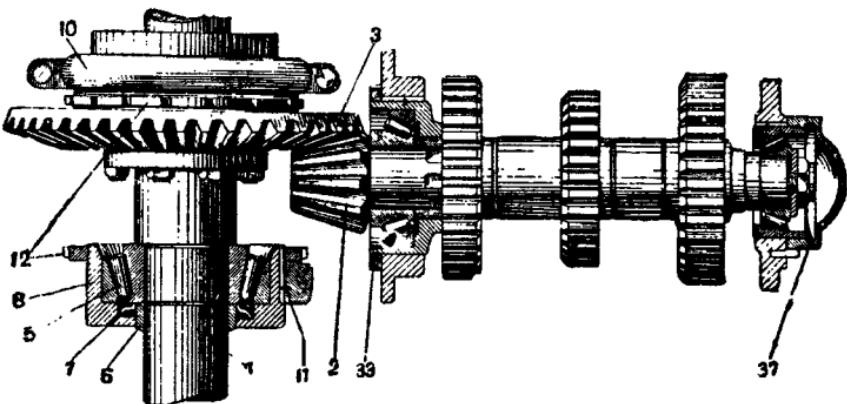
Регулировка конической передачи, подшипников, нижнего вала коробки передач и вала бортовых фрикционов.
